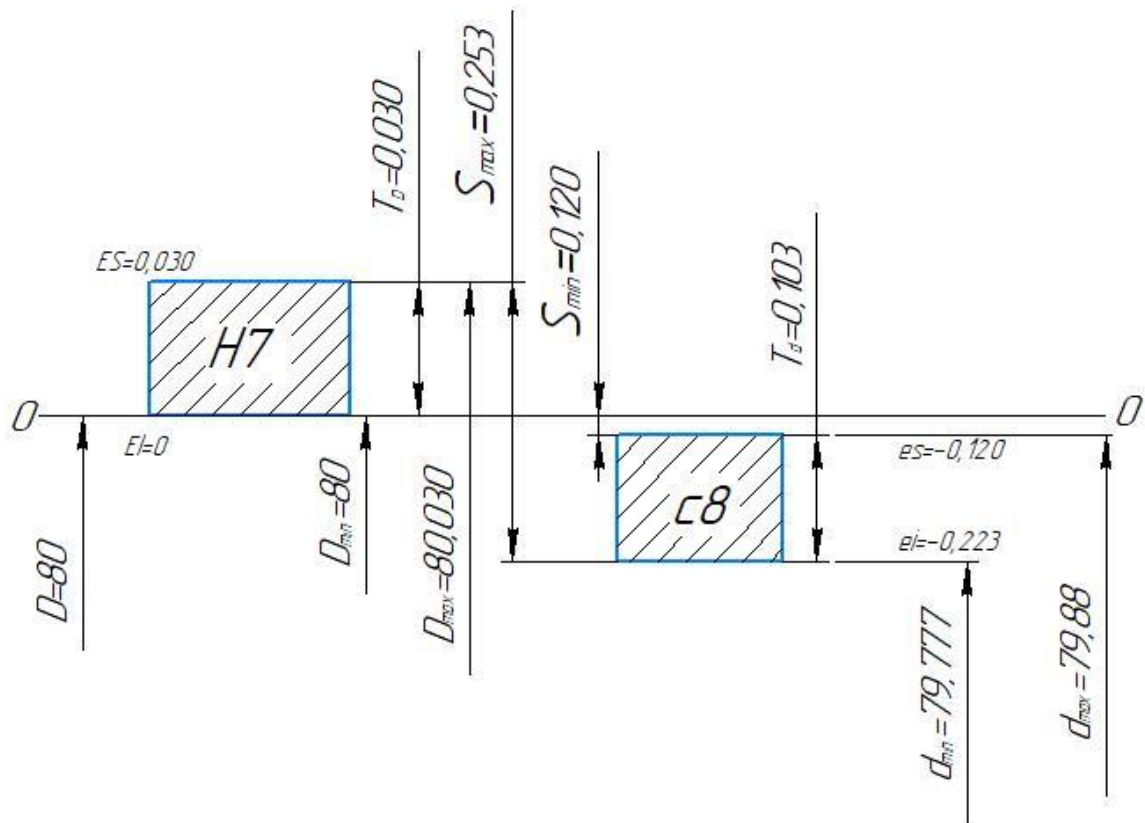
Схема розташування полів допусків посадки з зазором
